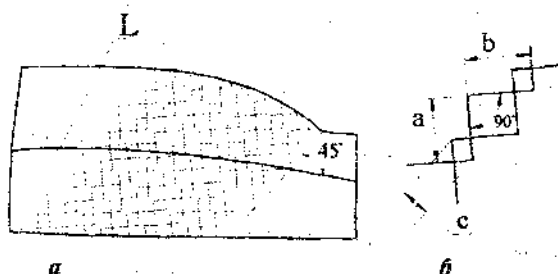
а – лопадка вентилятора; б – параметры строчки
